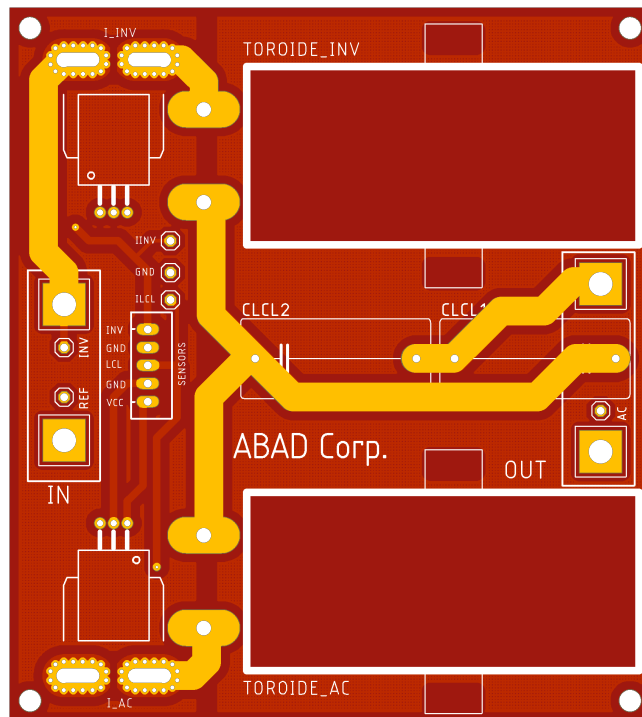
Vista previa del PCB en la capa superior antes de fabricar.
